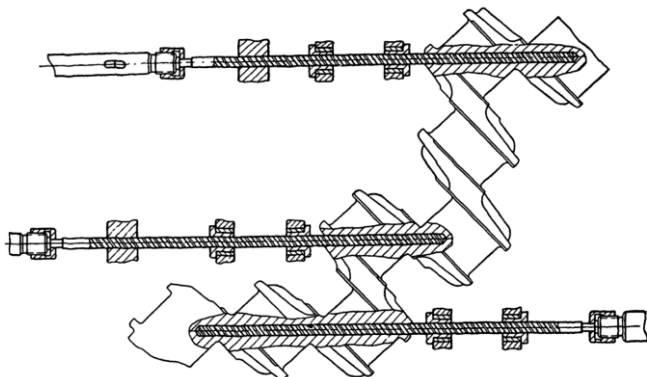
Схема одновременного сверления отверстий в шатунных шейках коленчатого вала
